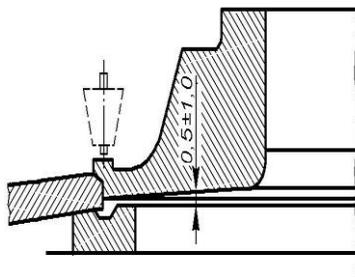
Сварное соединение фланца с буртиком и днищем
